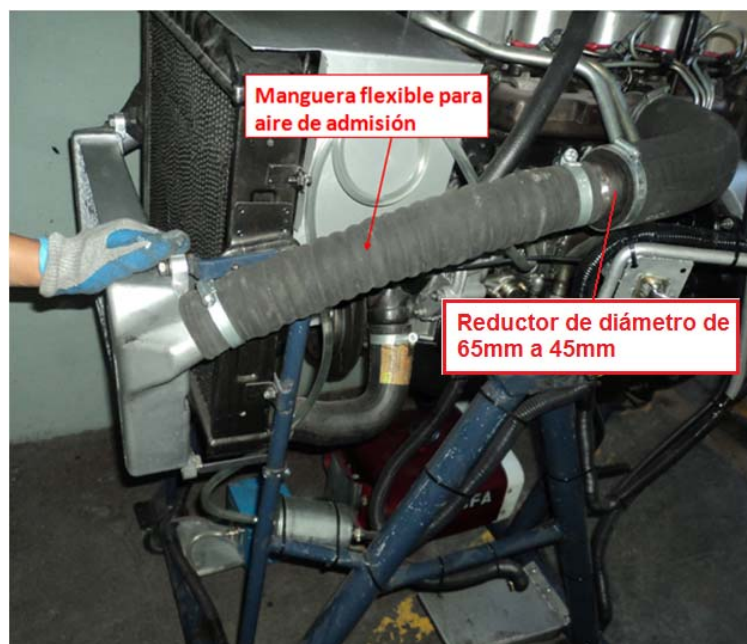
28 Unión de la salida del intercooler con la admisión del motor.
